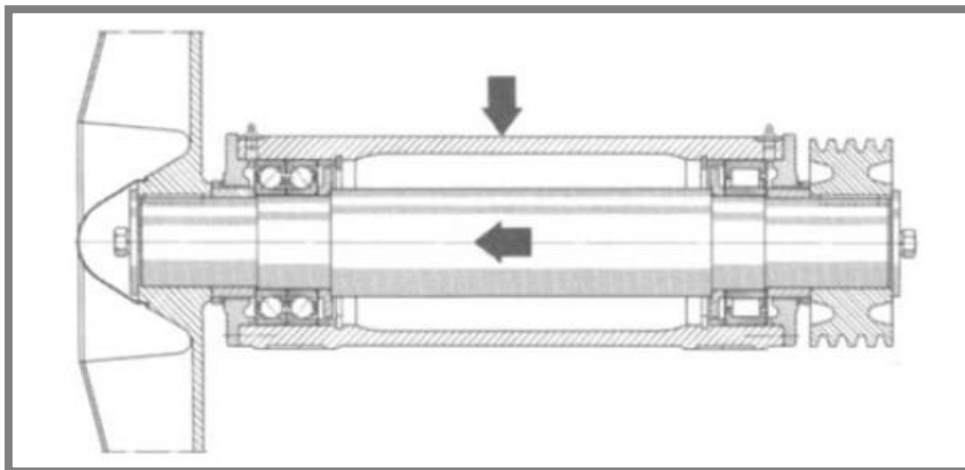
Dělená ložisková skříň ventilátorů s valivým ložiskem [10]
